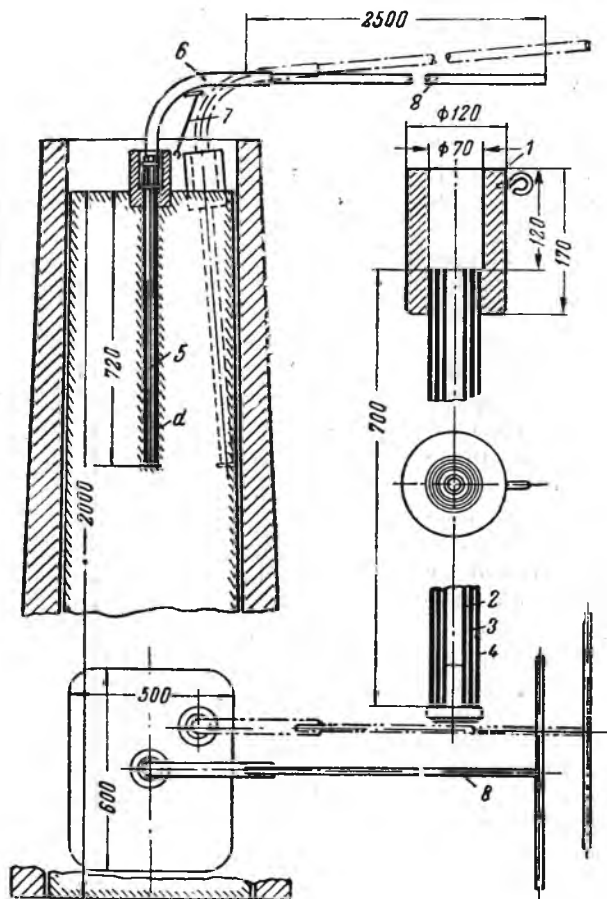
Гильза для термпар и приспособление для ее установки в жидкой стали
